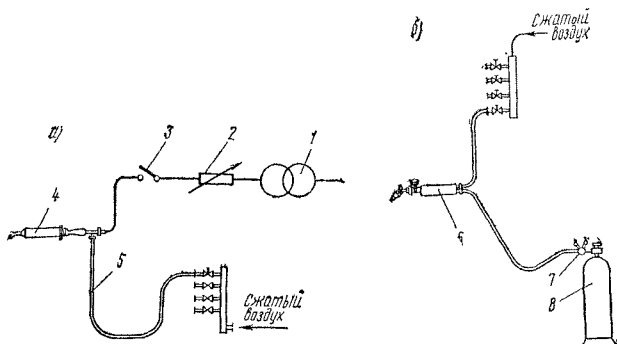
Схемы работы ручных нагревателей для прутковой сварки винипласта горячим воздухом
